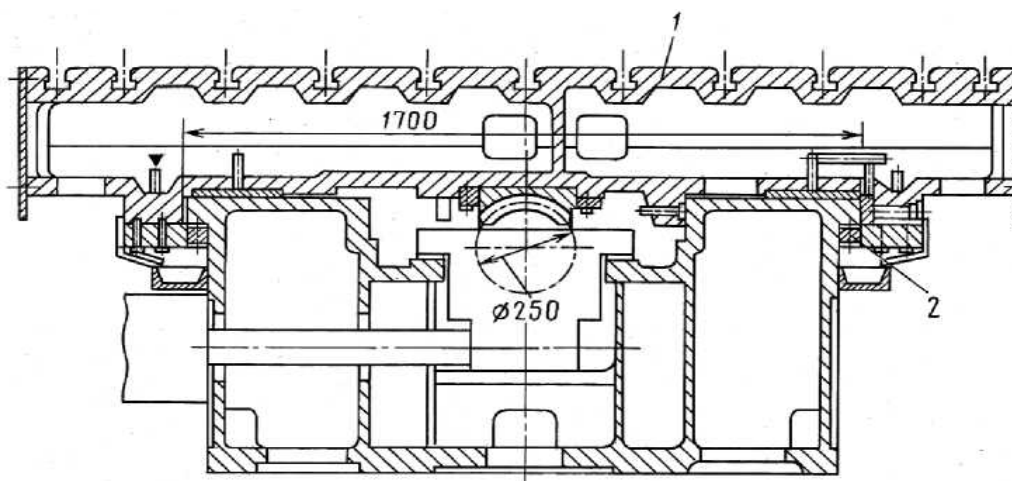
Гидростатические направляющие продольно-фрезерного станка
